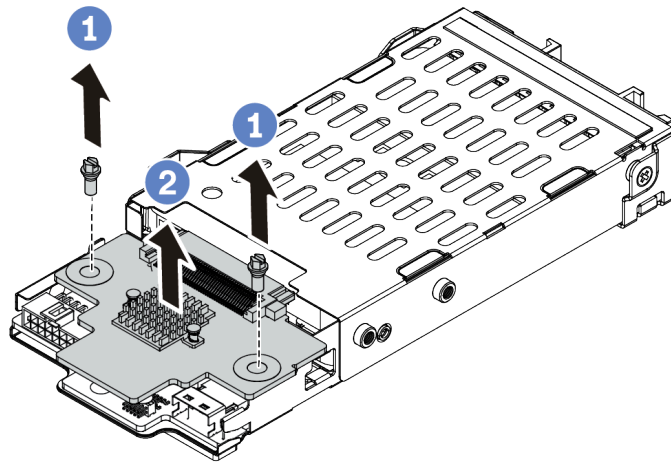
Retrait du fond de panier d'unité 7 mm (haut)
